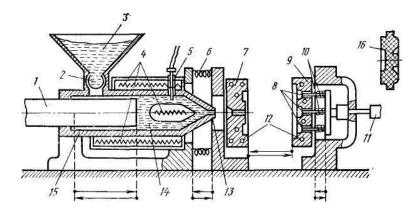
Схема литья под давлением на поршневой машине [15]: 1 – поршень; 2 – дозирующее устройство; 3 – бункер; 4 – устройство электроподогрева; 5 – терморегулятор; 6 – пружины; 7 – часть пресс-формы; 8 – выталкиватель; 9 – часть пресс-формы; 10 – пружины; 11 – упор; 12 – каналы; 13 – сопло; 14 – камера сжатия; 15 – литьевой цилиндр; 16 – изделие
